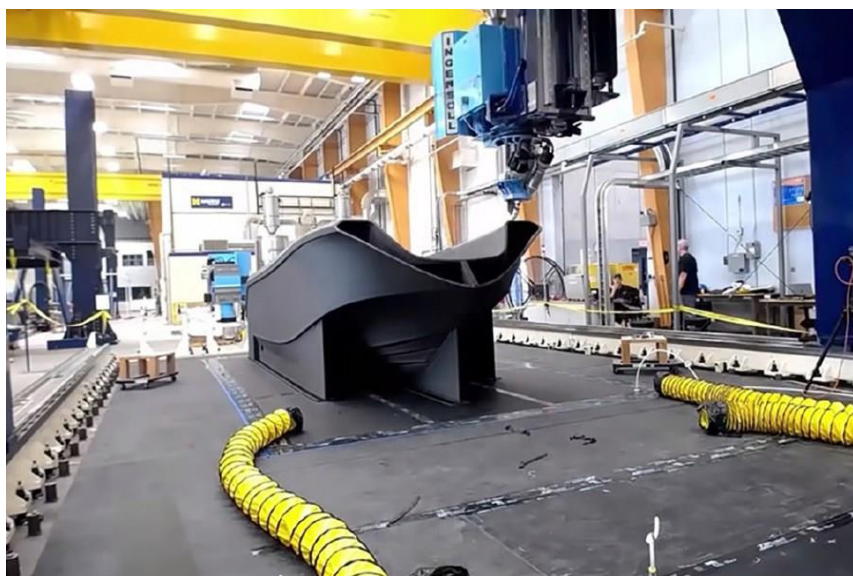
Изготовление корпуса катера с помощью 3D-печати.
